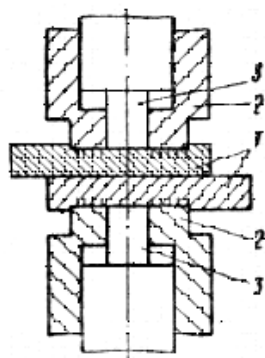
Схема сварки с предварительным зажатием деталей: 1 – свариваемые детали, 2 – прижимы, 3 – пуансоны.
